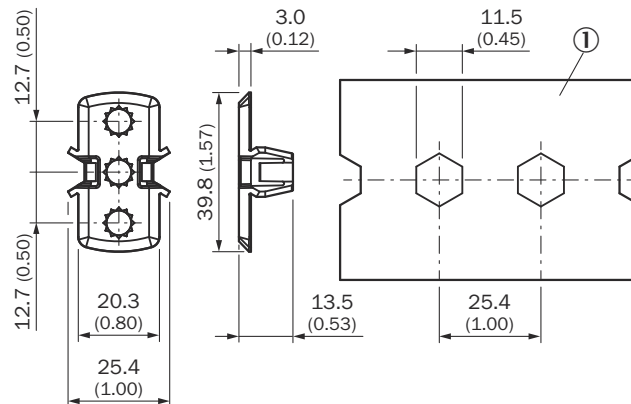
Cantoneiras de fixação POD (montagem entre seções hexagonais)
